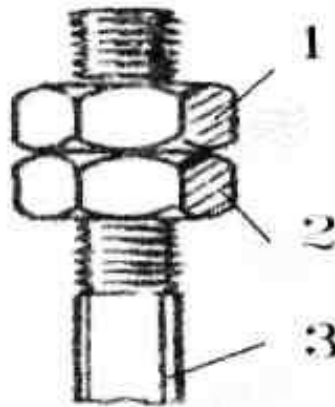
Пристрій з двома гайками: 1- гайка; 2- контргайка; 3- шпилька.
